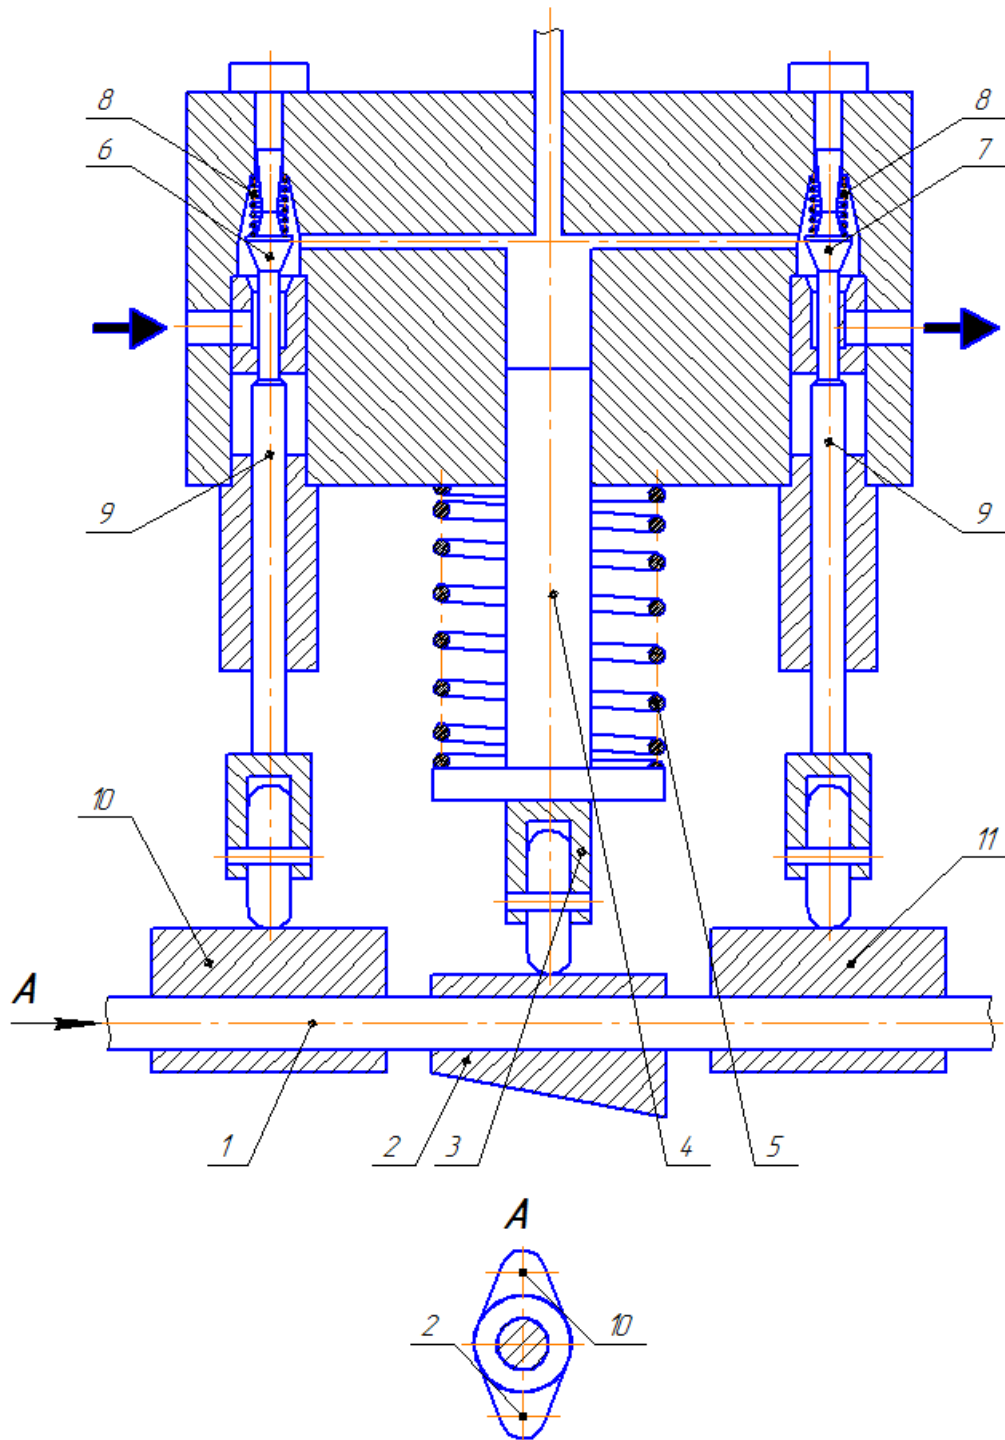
Паливний насос з клапанним регулюванням при наповненні надплунжерного простору паливом: 1 - розподільний вал; 2- плунжерний кулачок; 3 - штовхач; 4 - плунжер; 5 - поворотна пружина; 6 – наповнювальний клапан; 7 – відсічний клапан; 8 - клапанна пружина; 9 – штовхач; 10 – кулачок наповнювального клапана; 11 - кулачок відсічного клапана
